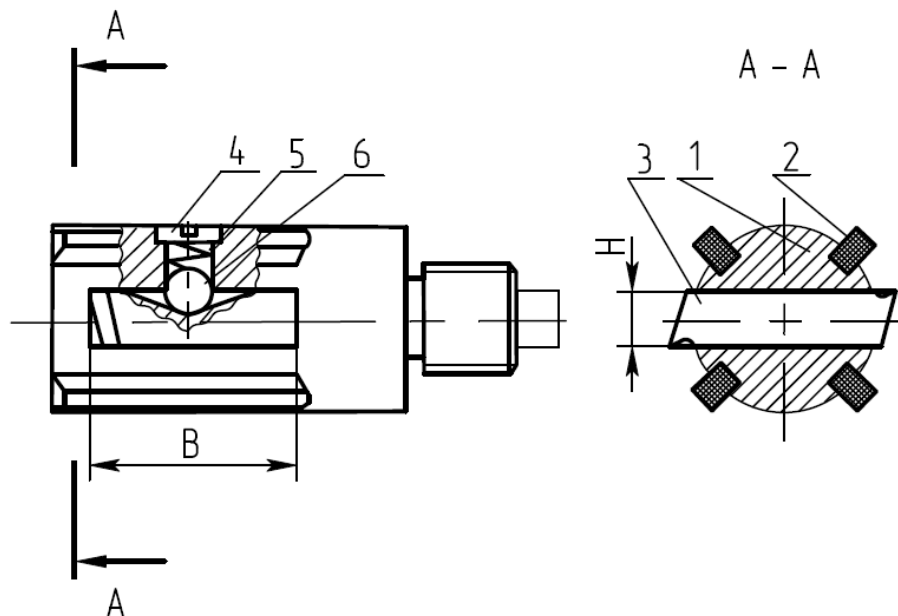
Плавающая двухрезцовая расточная головка: 1 – оправка, 2 – направляющая шпонка, 3 – плавающий резец, 4 – штифт, 5 – пружина, 6 – шарик
